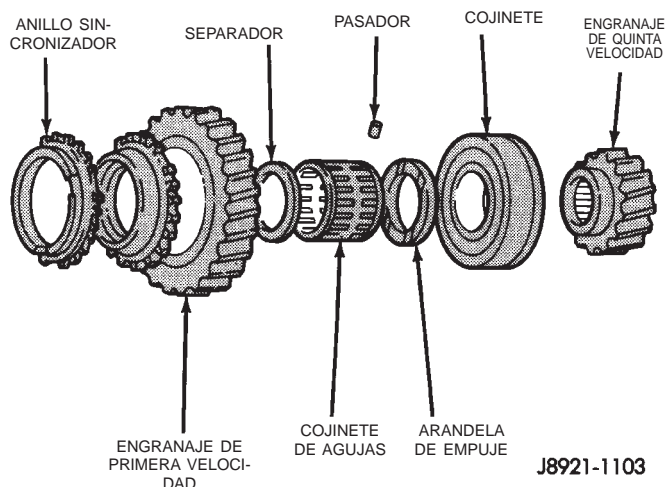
Componentes de engranajes de primera y quinta velocidad
